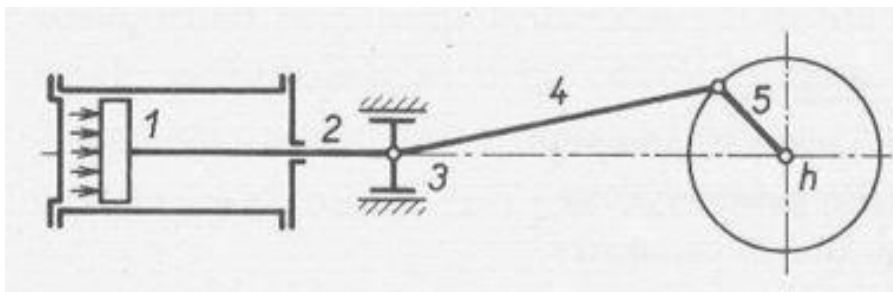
Kloubový mechanismu – hnětací stoj [9]
